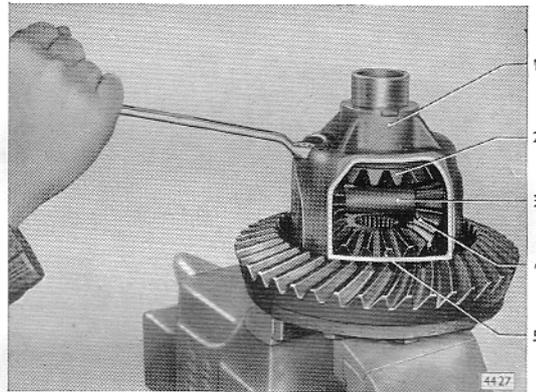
Sicherungsschraube für Ausgleichkegelradachse anziehen
